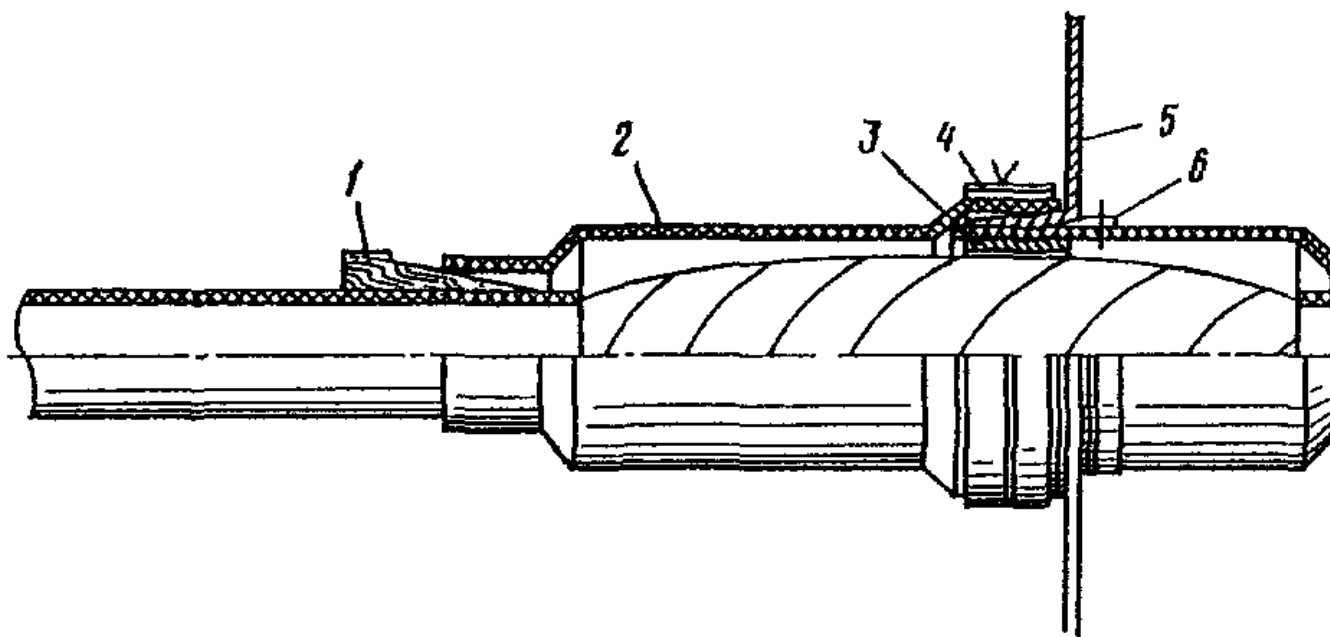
Муфта, подготовленная к сварке: 1 - деревянные клинья; 2 - полиэтиленовая муфта; 3 - опорное металлическое кольцо; 4 - бандаж из резиновой ленты; 5 - медный вкладыш; 6 - бандаж из кабельной бумаги
